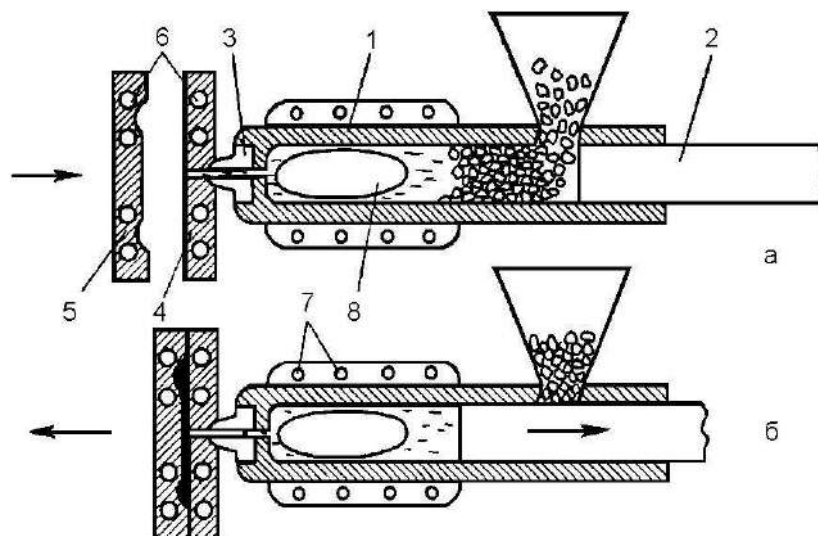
Литьевая машина: а – форма открыта; б – форма с изделием закрыта;
